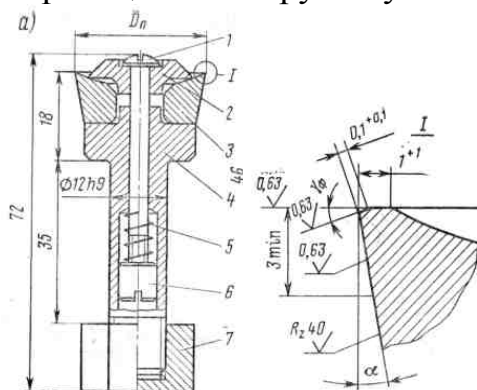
Конструкция сборного чашечного резца со стандартной пластиной (а) и геометрические параметры его режущей части
